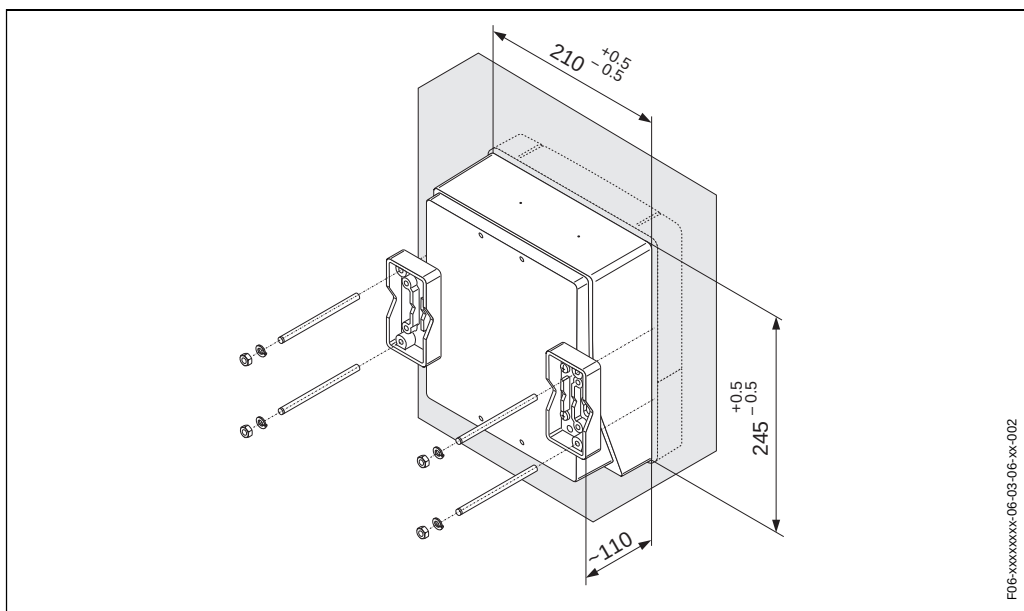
Instalacao no painel (alojamento com montagem de parede)
